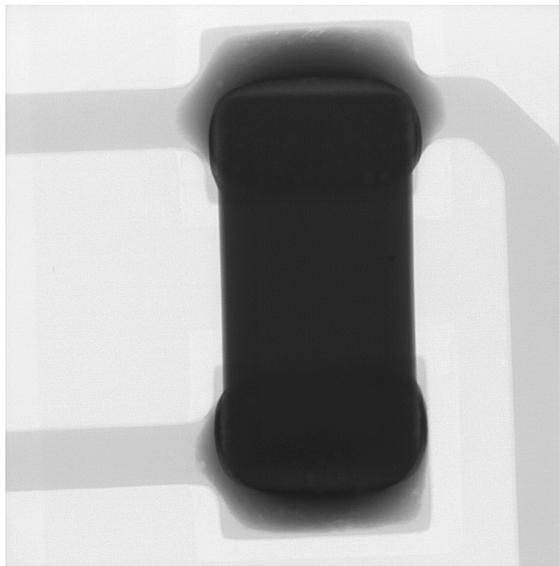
Capacitor soldado sin defectos en las soldaduras.
